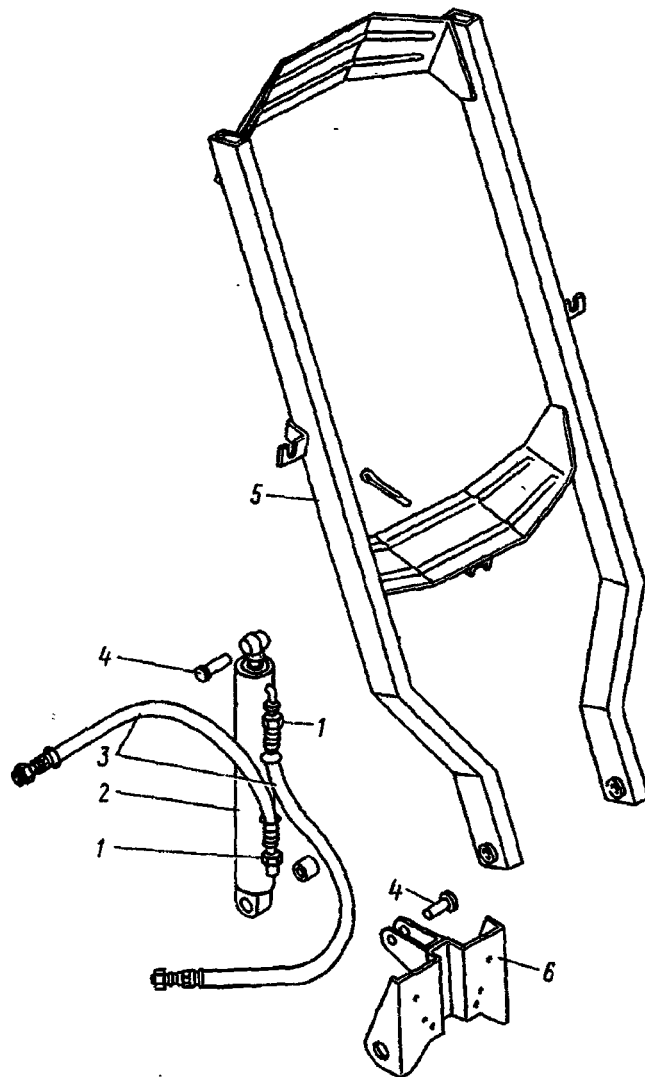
Гидроцилиндр механизма подъема запасного колеса:
